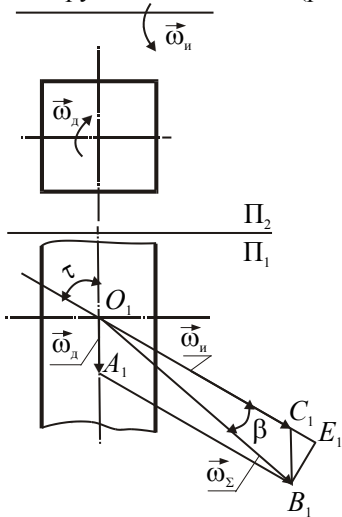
Схема обробки багатогранного вала при перехресних осях інструмента і заготовки
